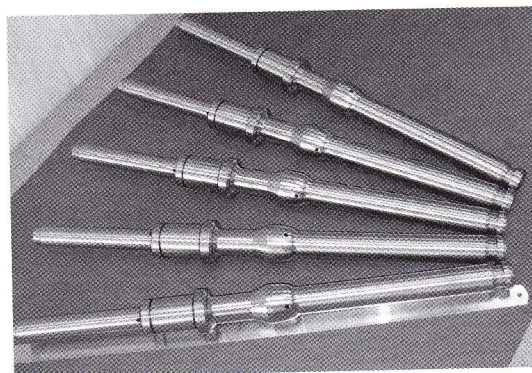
Запорно-регулирующие элементы для напорных клапанов гидрораспределителей рабочих гидроцилиндров пресса НП-130
